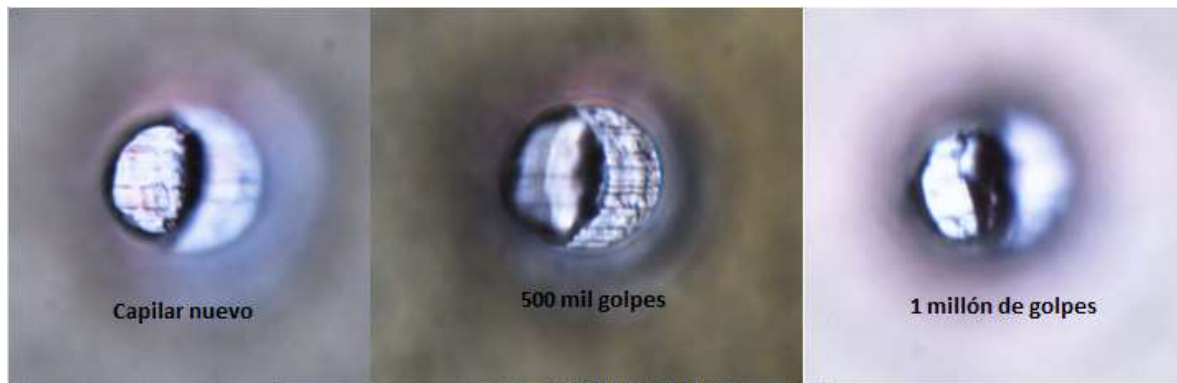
Corte de Bump Double Smooth, durante vida útil de capilar. [2]
